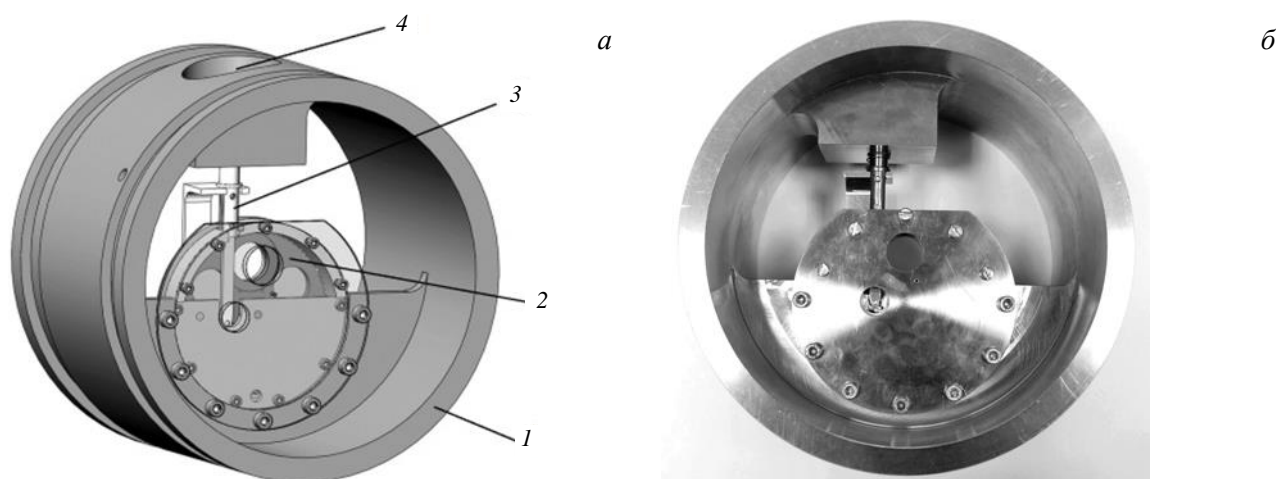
Трёхмерная конструкторская модель (а) и внешний вид (б) механизма смены плёнки анализатора LENPA: 1 — корпус центрального электрода ускорительного модуля; 2 — вращающийся диск (кассета) с плёнками; 3 — электромагнитный привод механизма; 4 — катушка электромагнитного привода
